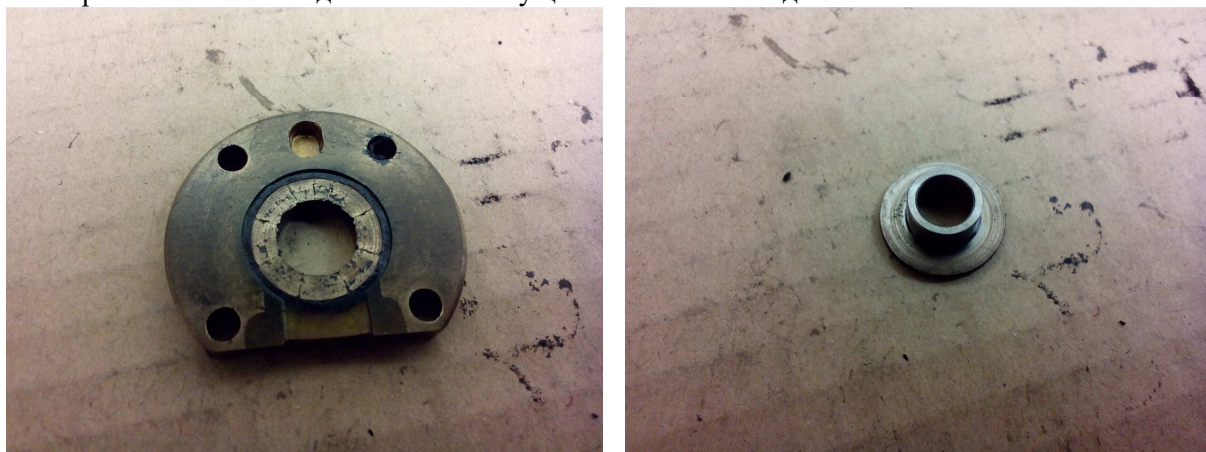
Фото деталей упорного подшипника турбокомпрессора после отказа
